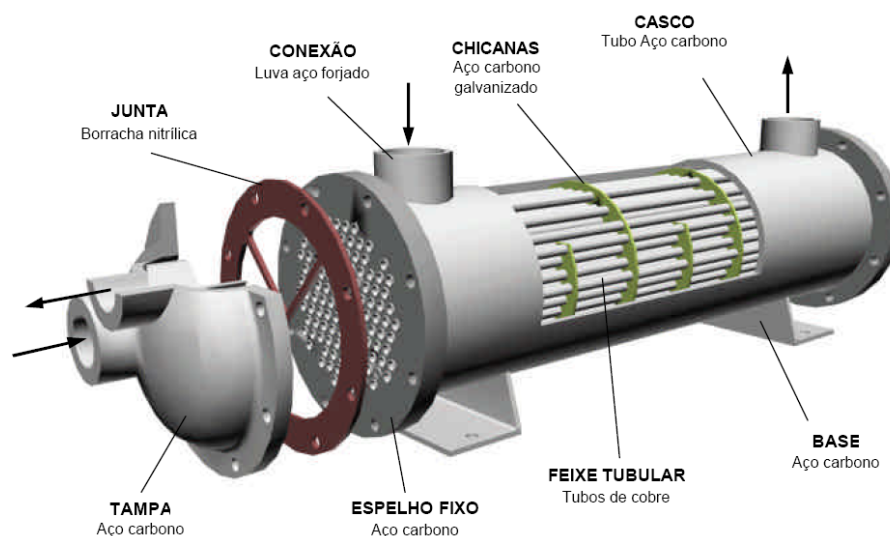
Vista explodida de trocador de calor do tipo casco-tubos [8].
